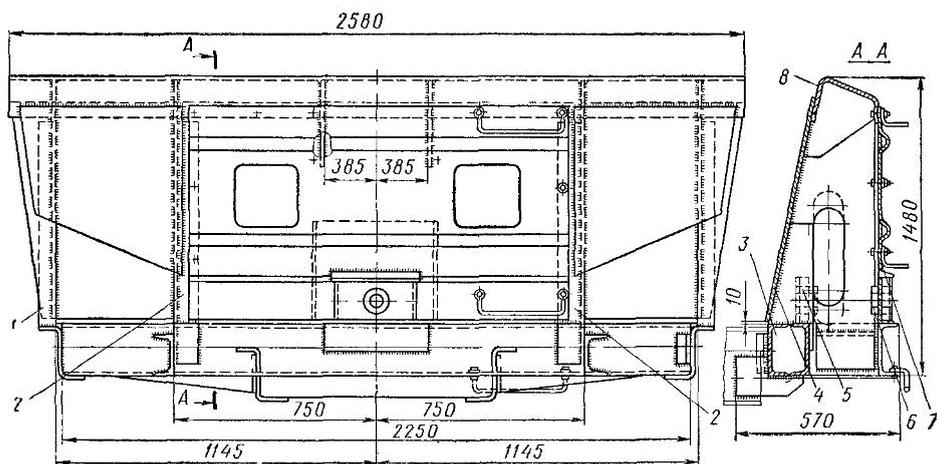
Лобовая стенка кузова вагона-самосвала 2BC-105
